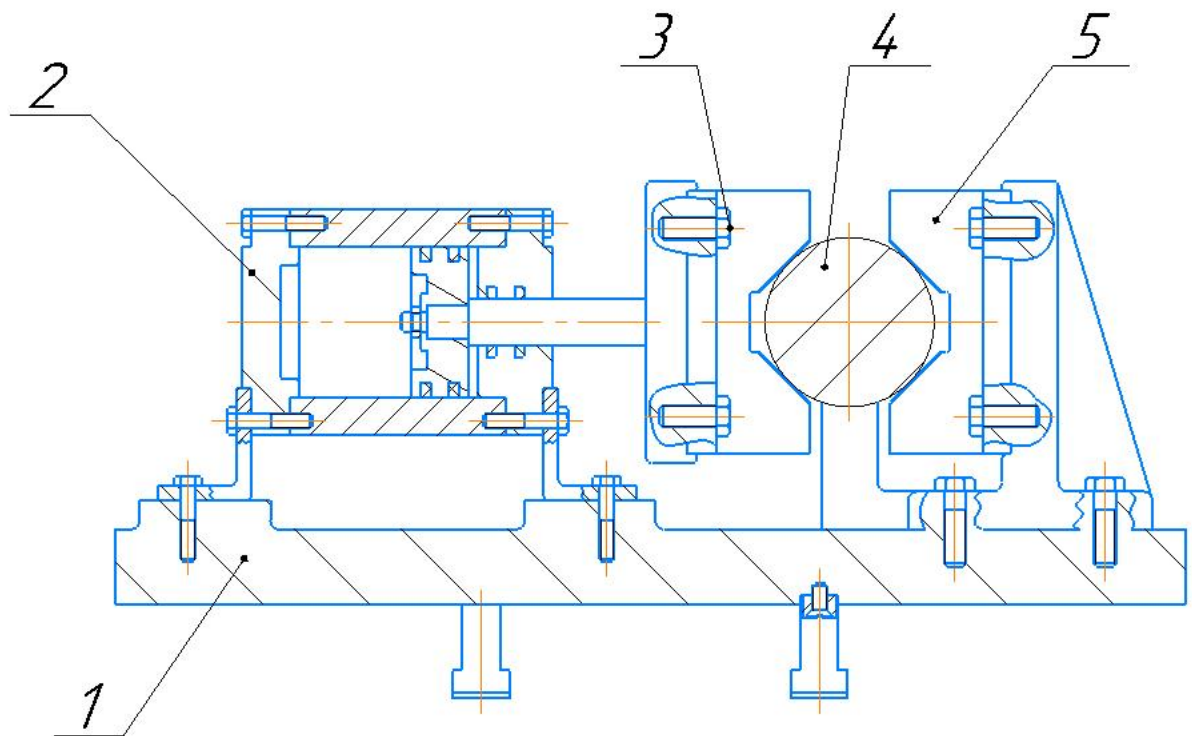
Пристосування для фрезерування шпоночного пазу
